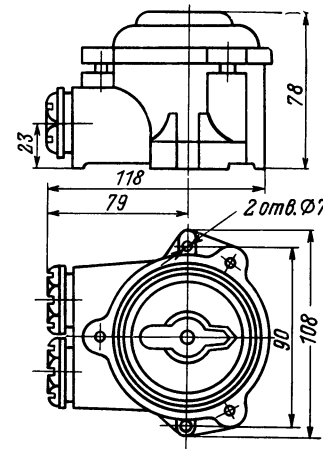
Пакетный выключатель ГПВМ2-10.
